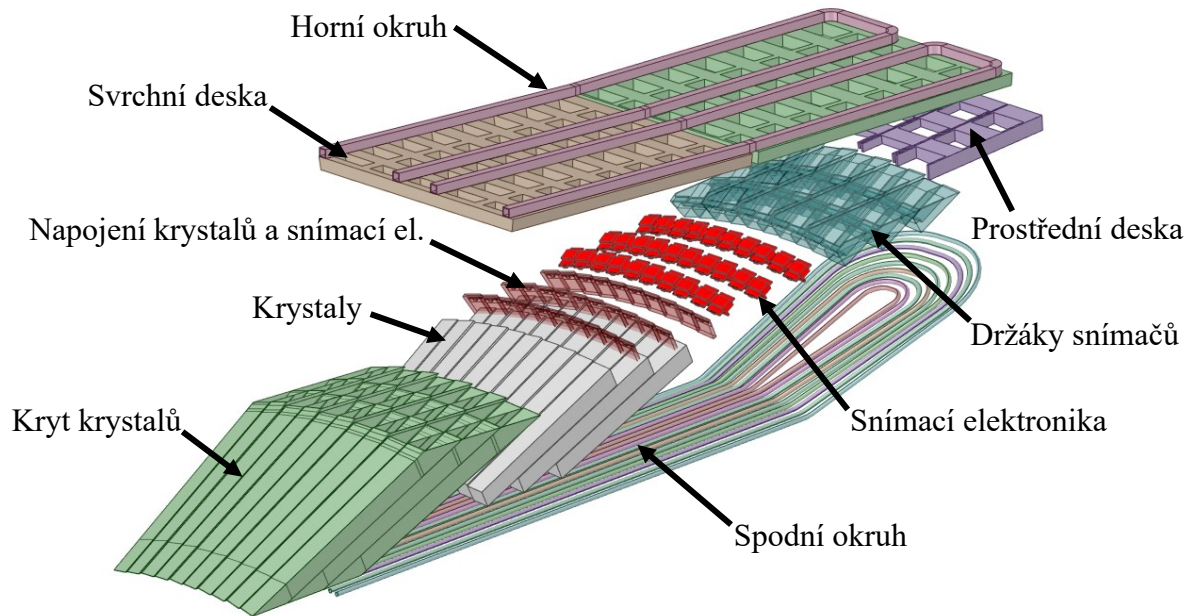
Prototyp segmentu s měřicí technikou [4]
